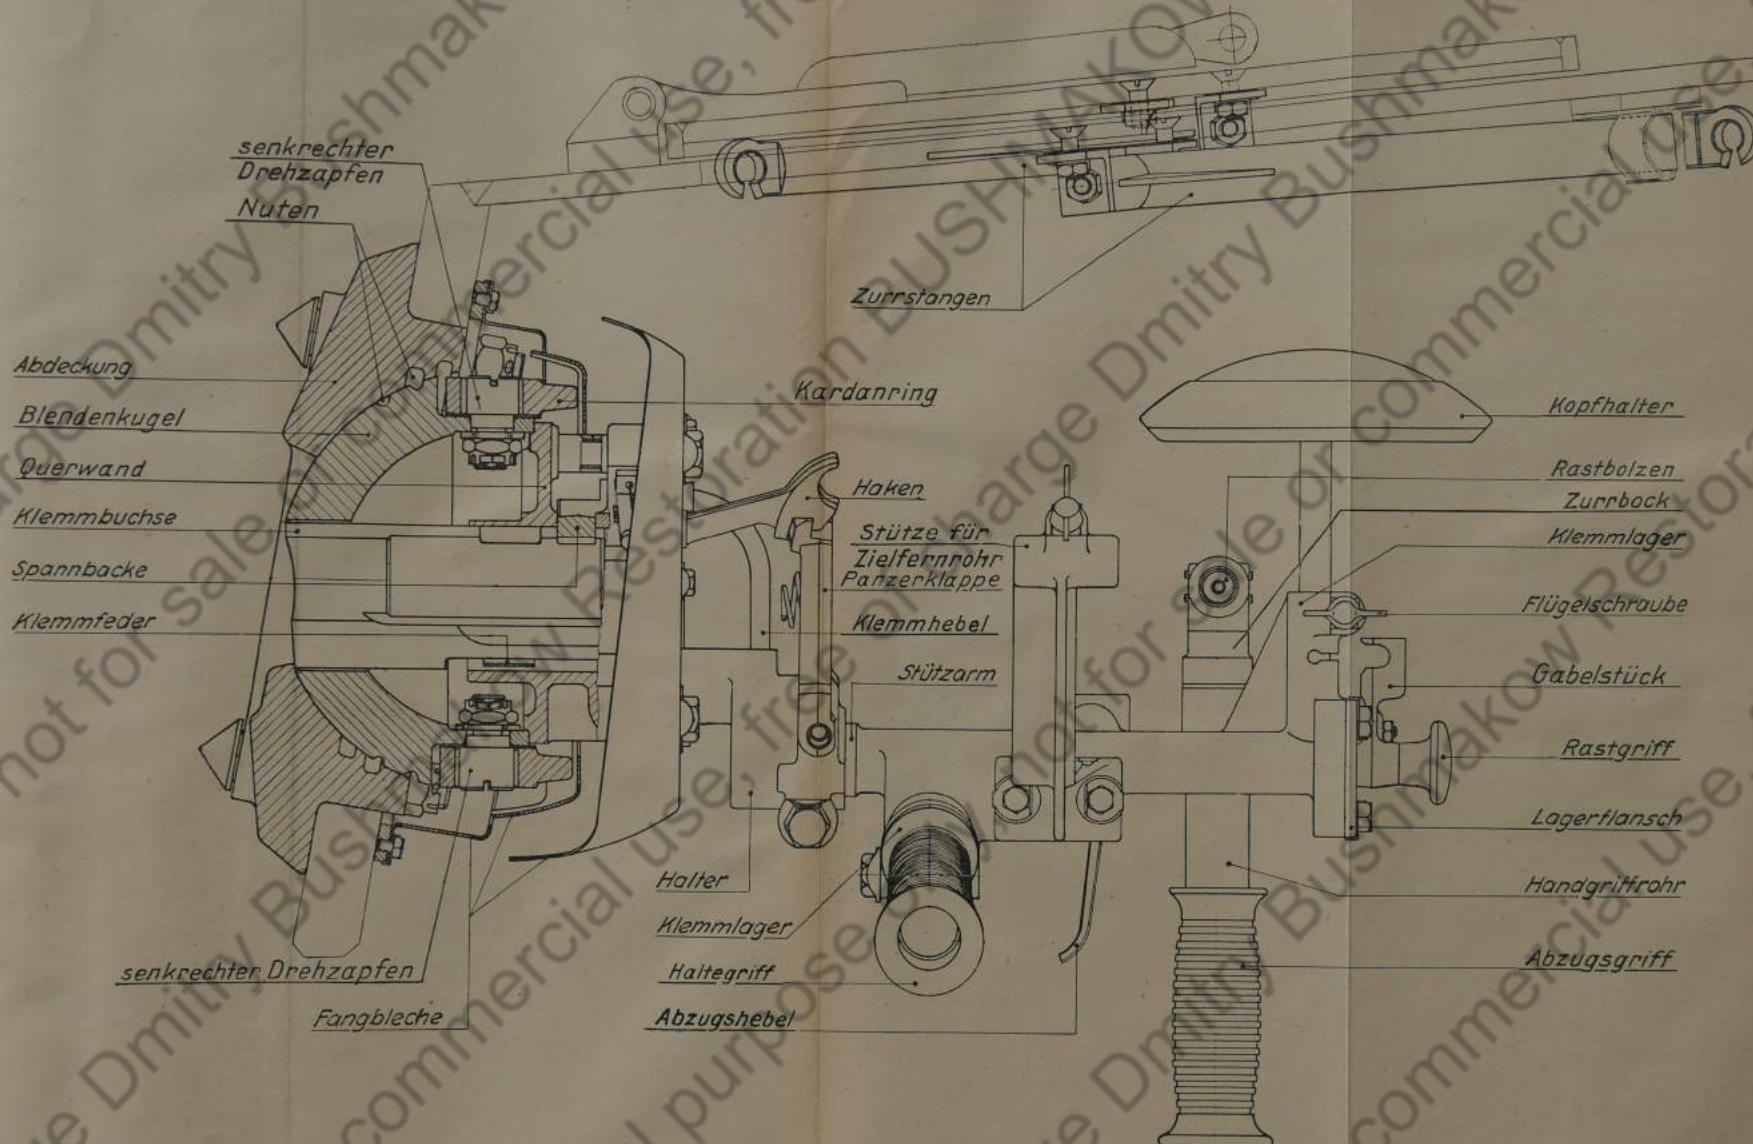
Kugelblende 30 für MG 34 mit Patronentrommelzuführung
